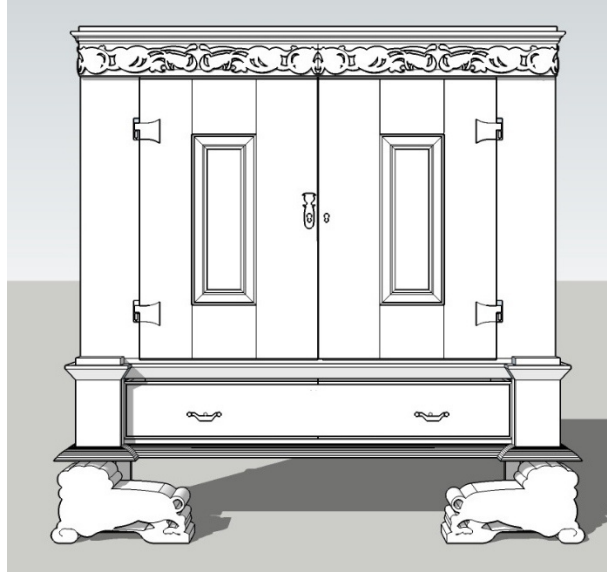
Vista do alçado anterior ou frontal do armário. Fonte: própria
